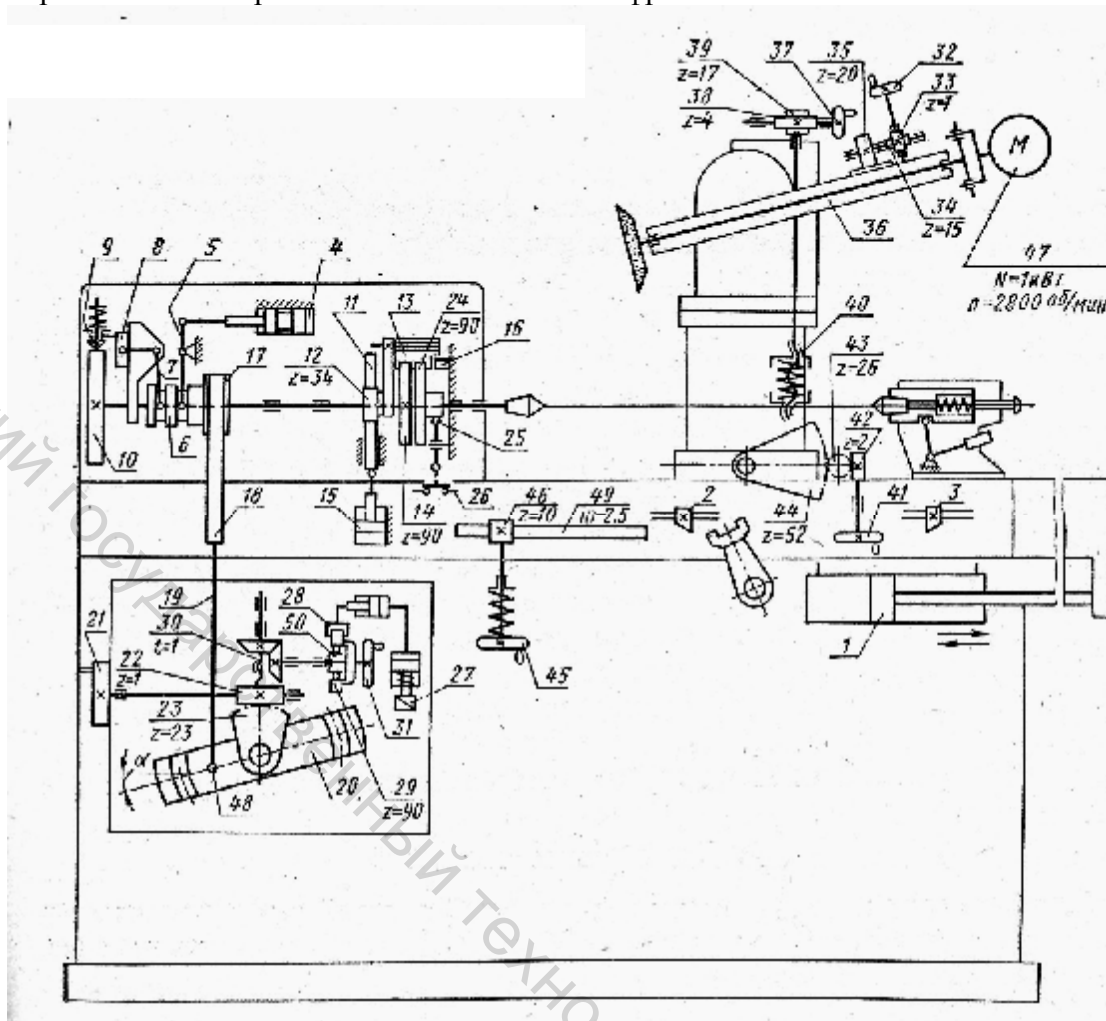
Кинематическая схема полуавтомата для заточки червячных фрез.
